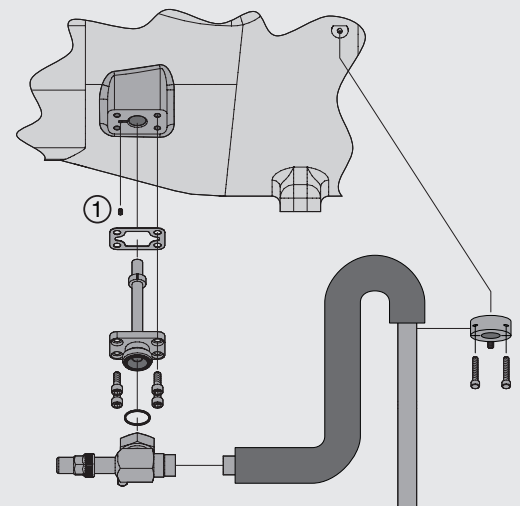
Патрубок ECO с запорным клапаном и гасителем пульсаций
